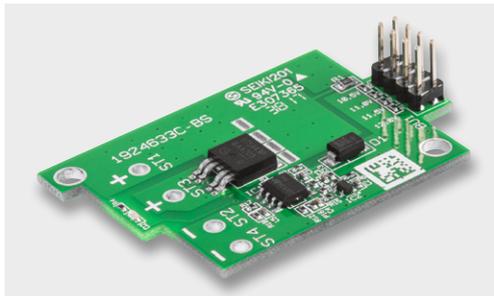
Platine mit eingelöteter 8-poliger Stiftleiste zur Aufnahme des Kodiersteckers
